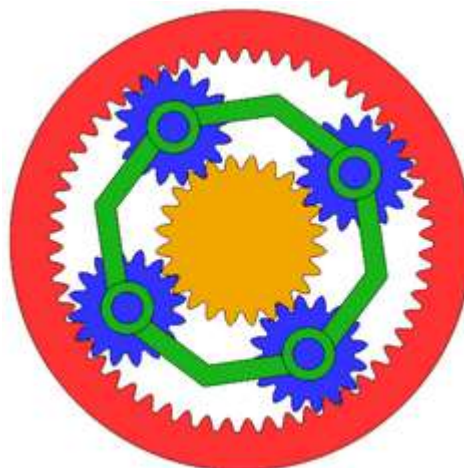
Пример закрытой шестерни - водило в планетарной передаче
